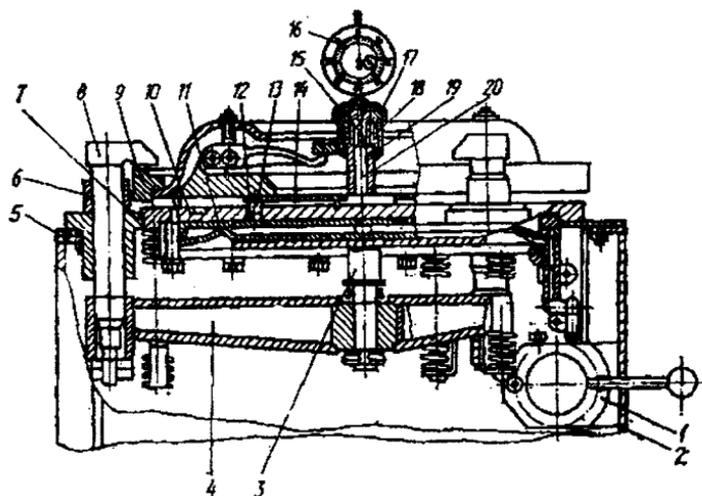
Стенд для разборки, сборки и регулировки сцеплений мод. ЦКБР-207 (ЗИЛ, ГАЗ)
